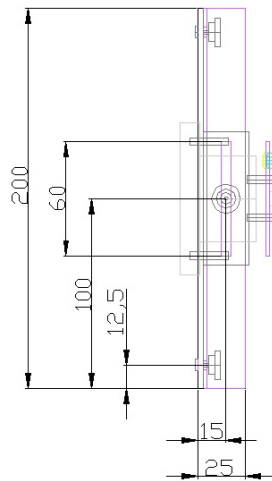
, Grundriss Schirm mit Anzeige
